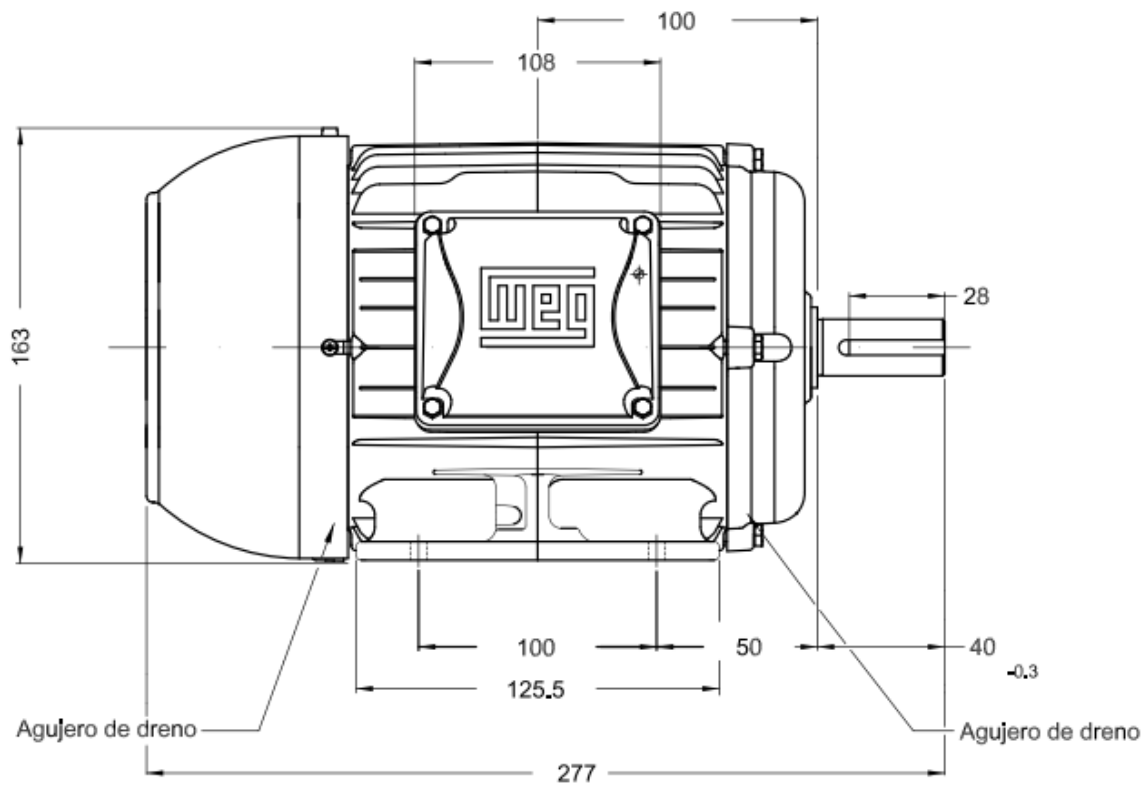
Vista lateral izquierda del motor con sus dimensiones
